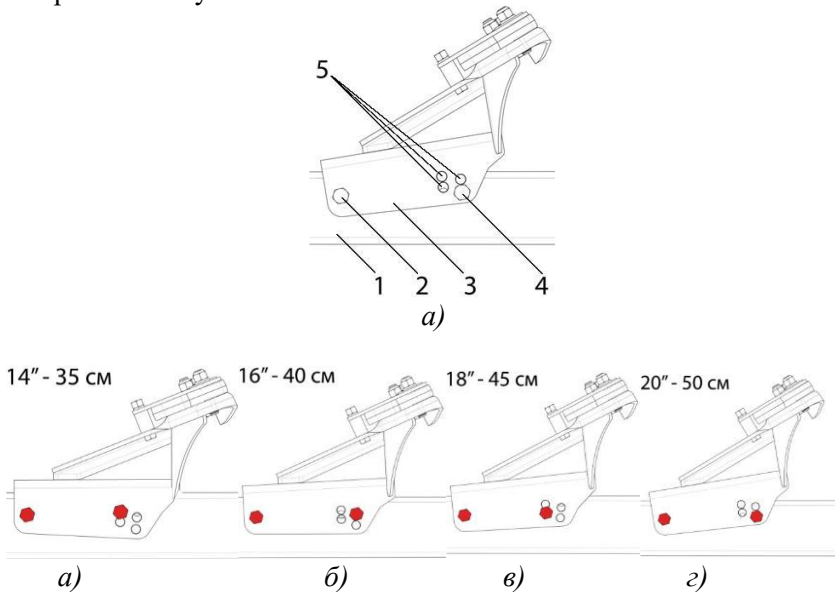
Схема установки кронштейна кріплення корпусу плуга при регулюванні його ширини захвату:
